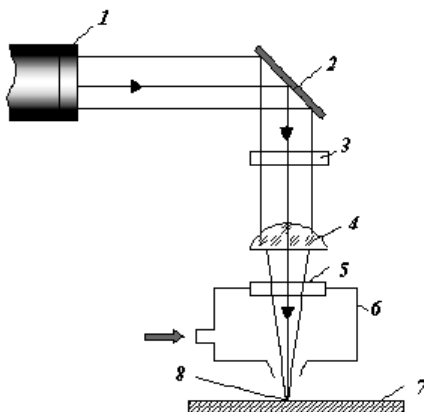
Схема лазерной резки с подачей газовой струи в зону воздействия лазерного луча: 1 – лазер; 2 – зеркало; 3 – заслонка; 4 – линза; 5 – окно; 6 – камера; 7 – изделие; 8 – точка фокуса
